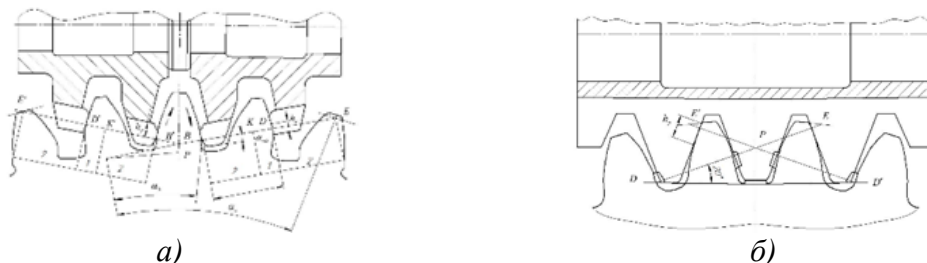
Визначення сумарного периметра одночасно різальних кромки: а - для черв'ячної фрези з роздільною схемою формоутворення; б - для стандартної фрези
